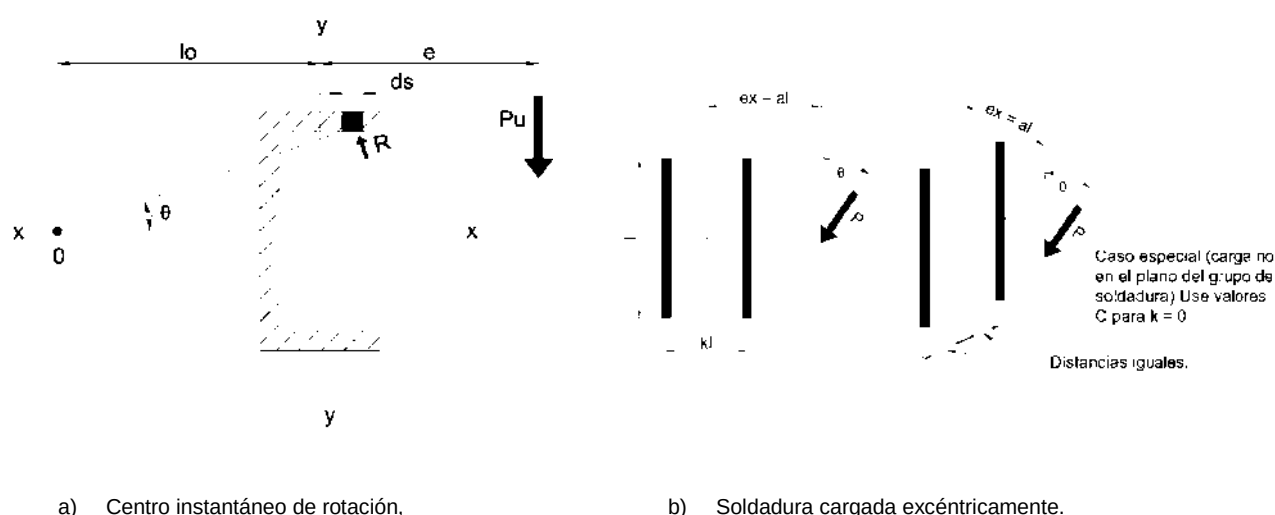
13 Soldadura cargada excéntricamente (AISC, 2010).
